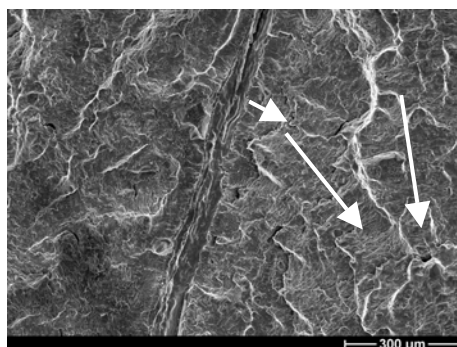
Örtliches Risswachstum des Fehlers 18 (Ausschnitt b aus Bild 4.4)
